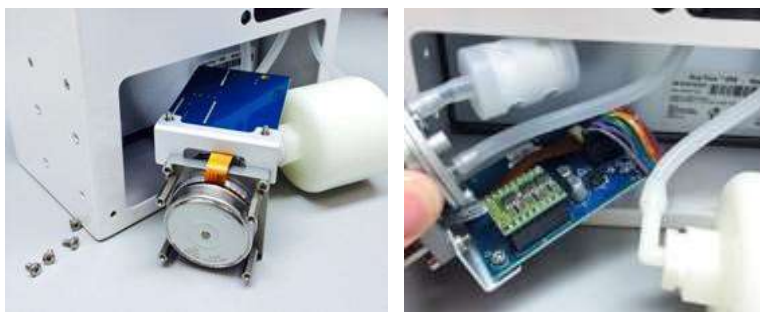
Saque la bomba de la carcasa y desconecte la tubería, el silenciador y el cable
